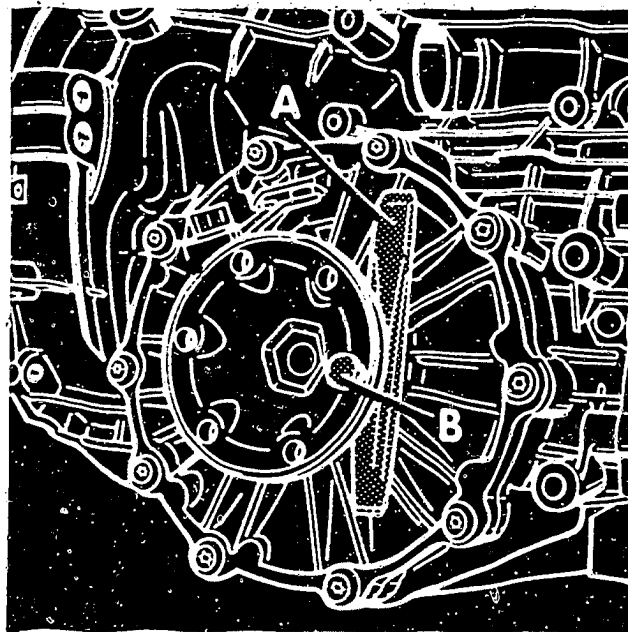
Zum Abdrücken der Seitenwellenflansche ist ein Meissel (A) zwischen Flansch und Gehäuse einzulegen und der Flansch mit der Schraube (B) abzudrücken.
